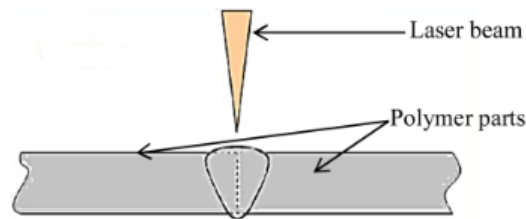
Ilustração de um processo de soldadura a laser direta [1].
